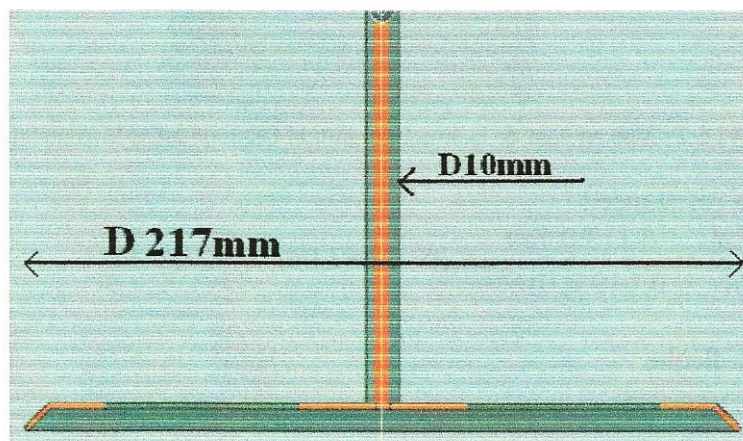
Vue en coupe du système de presse montrant les dimensions principales.
